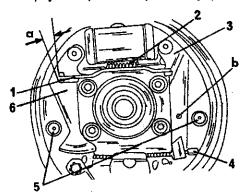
, Установленные тормозные колодки тормоза Bendix. "a" — упомянутый в тексте зазор.
